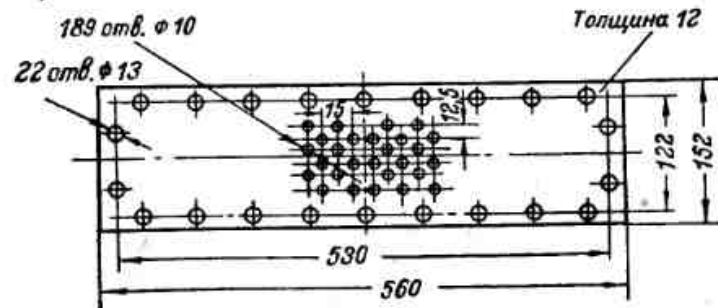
К расчету прямоугольной трубной доски, не подкрепленной связями.
